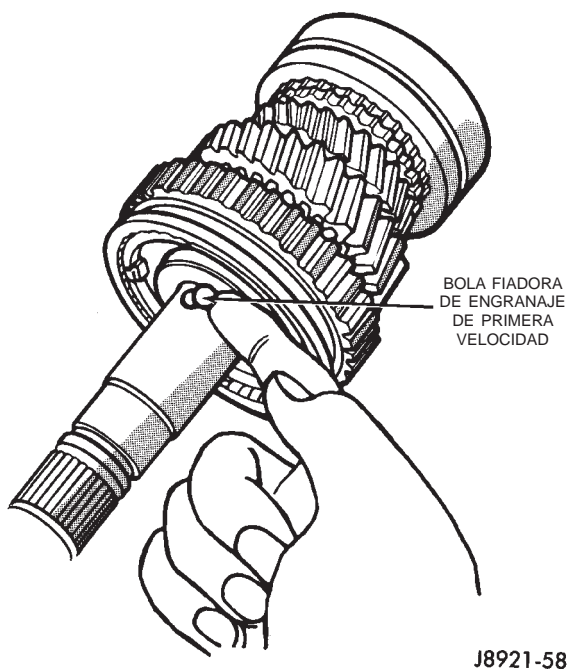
Instalación de bola fiadora de pista de rodamiento interior de cojinete de engranaje de primera velocidad
